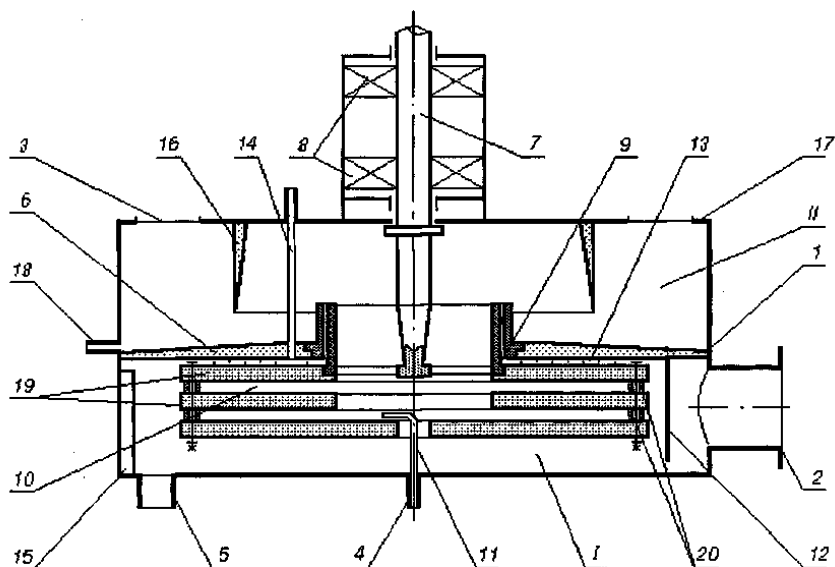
Схема роторно-импульсного аппарата: I – рабочая зона; II – сепарационная зона; 1 – корпус; 2 – патрубок для подвода газа; 3 – патрубки для отвода газа; 4 – патрубок для подвода жидкости; 5 – патрубок для отвода жидкости; 6 – перегородка; 7 – вал; 8 – подшипники качения; 9 – ротор; 10 – насадка; 11 – ороситель; 12 – отражательный экран; 13 – орошаемое динамическое уплотнение; 14 – трубка для подачи жидкости в уплотнение; 15 – перегородки; 16 – брызгоотбойник; 17 – крышка сепарационной зоны; 18 – штуцер для отвода унесенной жидкой фазы; 19 – диски; 20 – дистанционные втулки.
